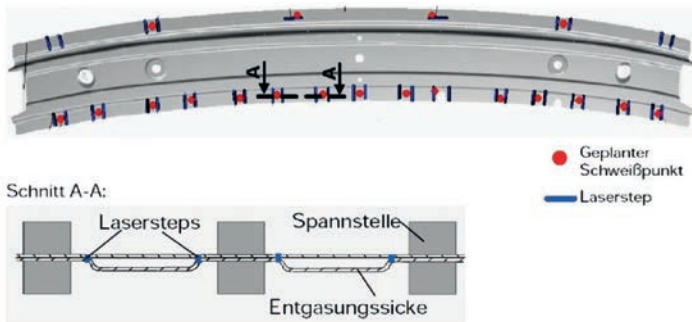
CO₂ Remote-Schweißen: Heckfensterrahmen mit Schweißstellen (oben), Entgasungsmöglichkeiten durch Einbringen von Entgasungssicken während des Tiefziehprozesses (unten) [Quelle: BMW].
